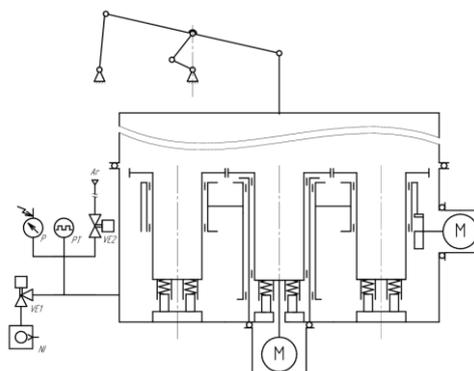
Вакуумно-кинематическая схема модернизации установки аргонодуговой сварки: CV – камера вакуумная, P – реле давления, PT – вакуумметр терморезисторный, VE1, VE2 – клапаны вакуумные электромагнитные, NI – насос пластинчатороторный
